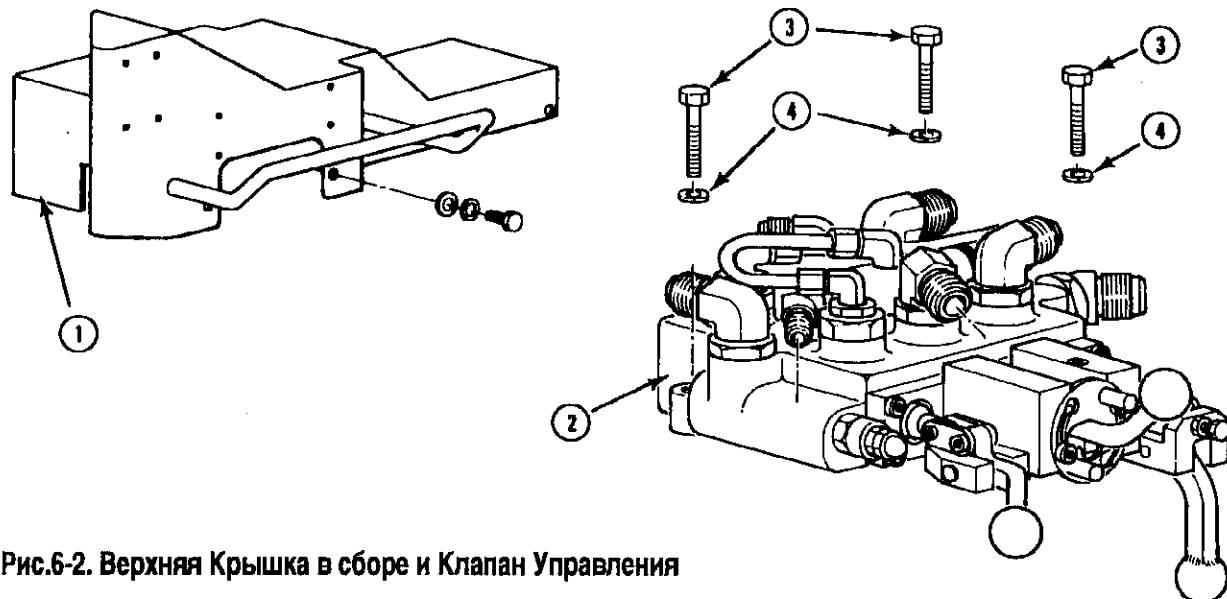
Верхняя Крышка в сборе и Клапан Управления
